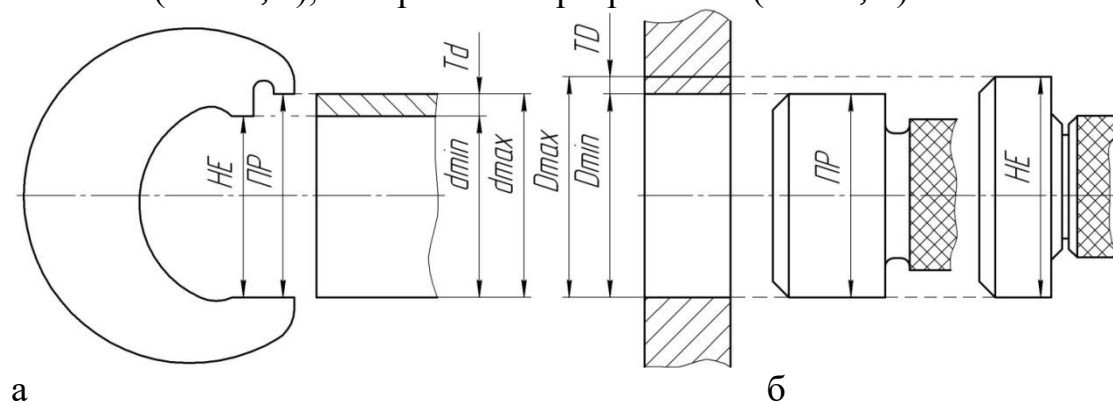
Контроль розмірів циліндричних поверхонь граничними калібрами: калібр-скобою; б – калібр-пробкою
